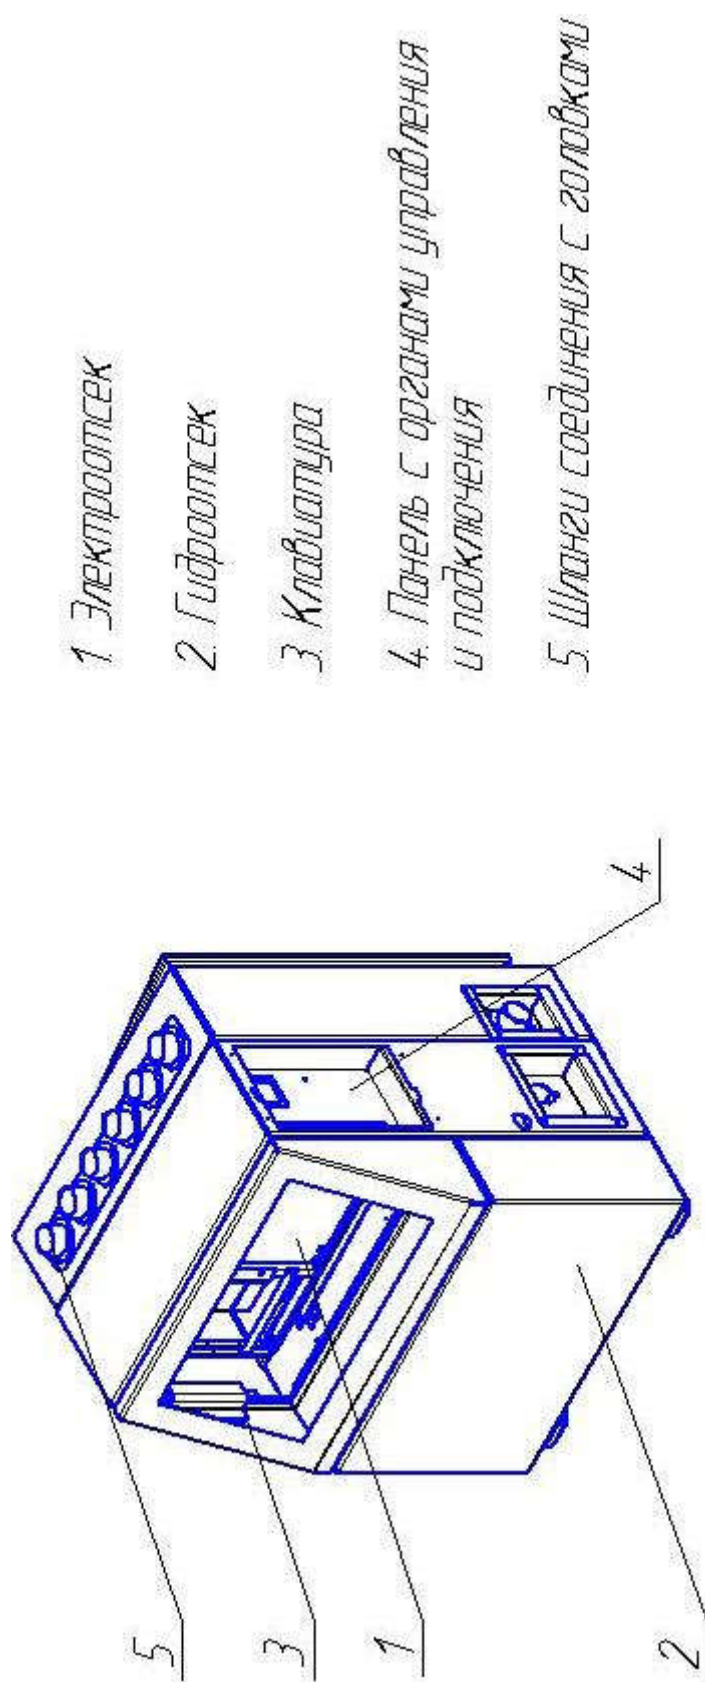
Корпус RT с корпусом «Дракон VI»
